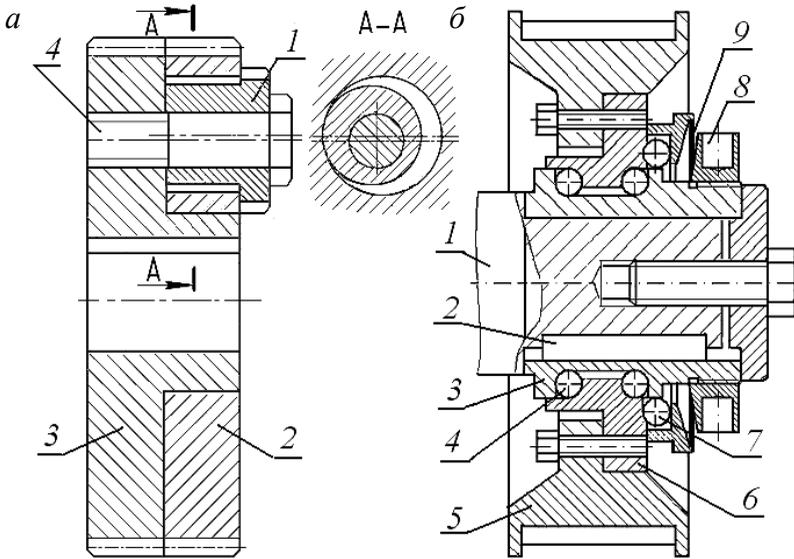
Безззорная передача с двумя зубчатыми колесами с эксцентриковой втулкой (а) и шариковая предохранительная муфта для зубчатых ременных передач (б)
